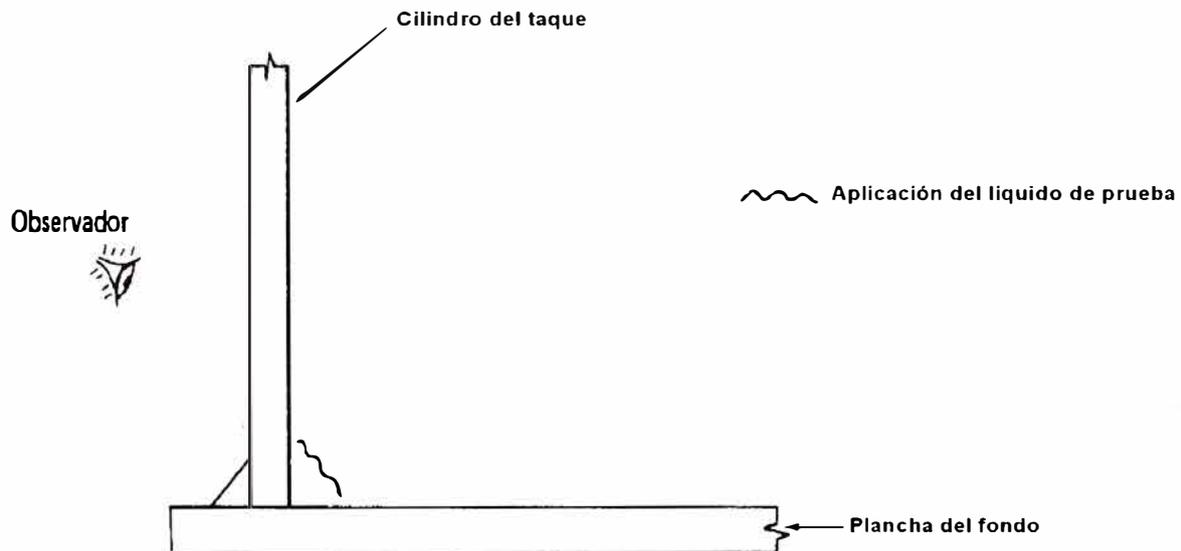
Prueba de soldadura en ángulo de unión fondo-primero anillo de tanques de almacenamiento
